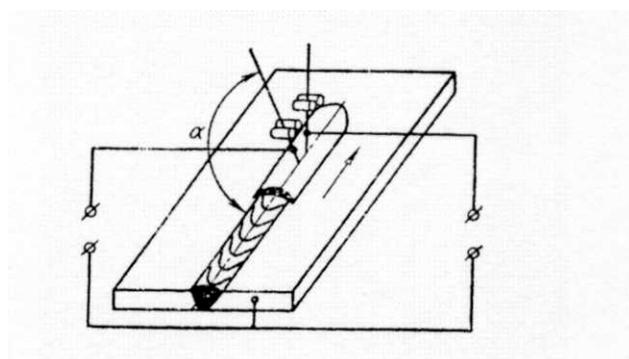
Схема образования шва при двухдуговой сварки
